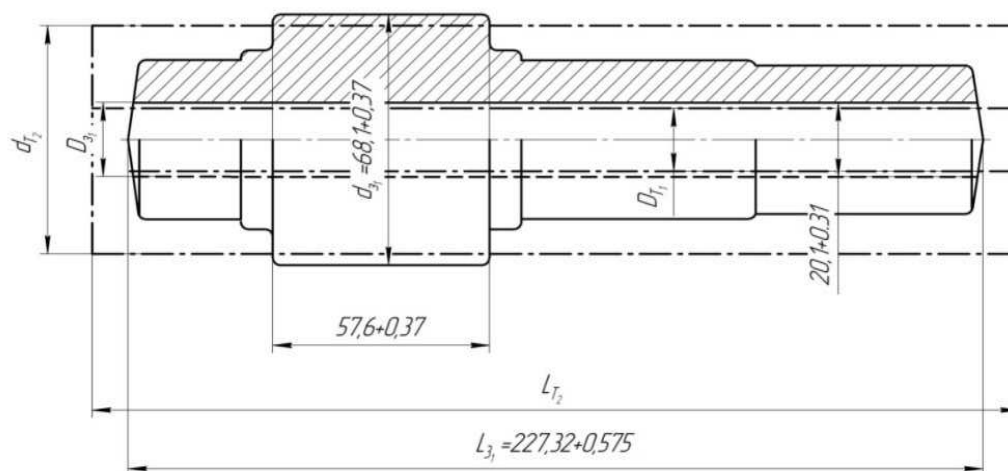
Эскиз заготовки, полученной из трубы большего диаметра d_{T2} и меньшей длины L_{T2} по сравнению с расчетными диаметром заготовки d_{31} и длиной L_{31} поковки вала по варианту 2.
